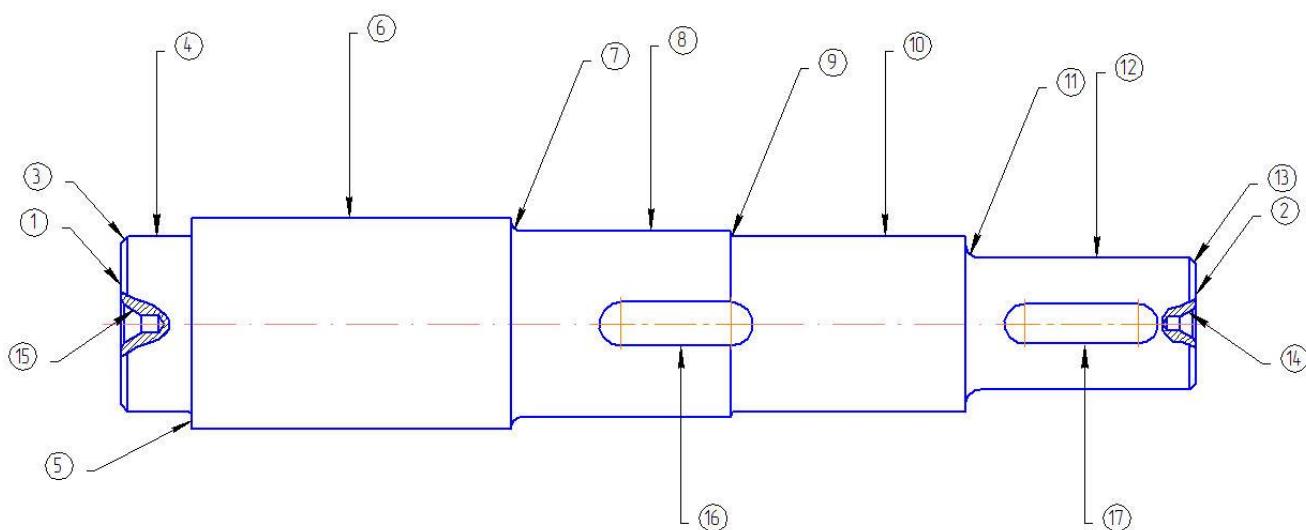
Оброблювані поверхні деталі «Вал»
